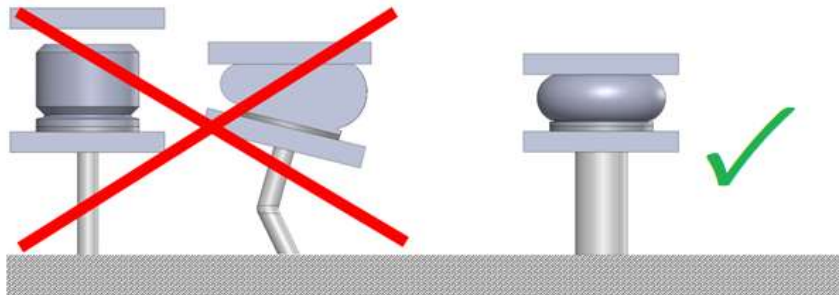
Unterbau stabil und Auflageflächen nach 4.3 auslegen
